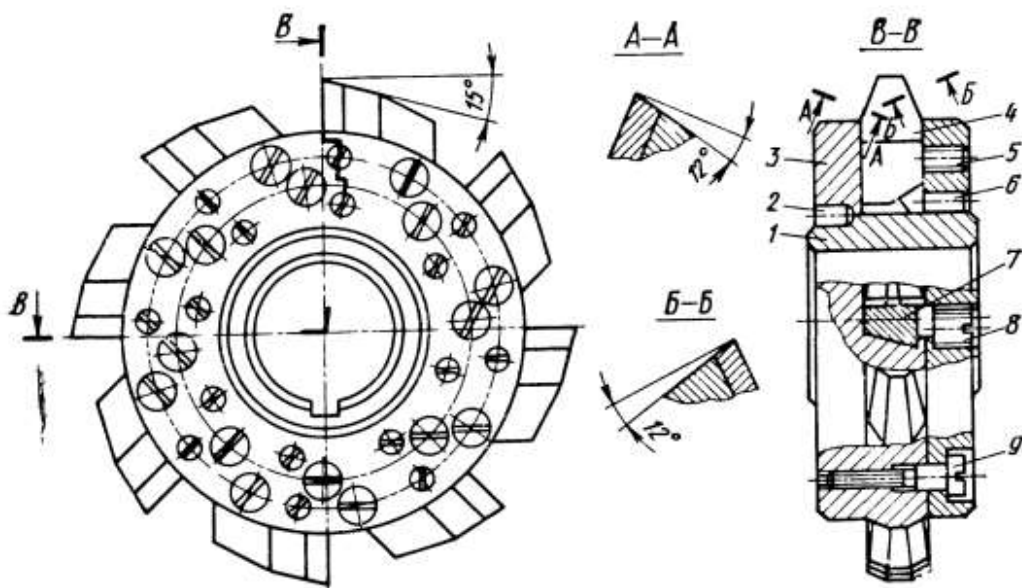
Дискова чорнова фреза з напаяними пластинами [5]
